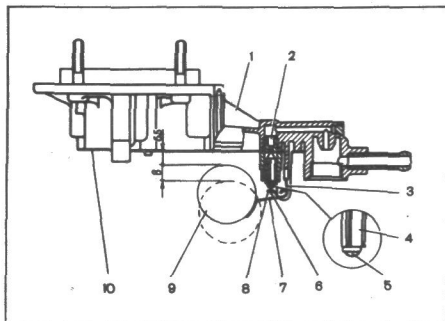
Установка уровня топлива в поплавковой камере карбюратора: 1 — крышка карбюратора; 2 — седло иглы клапана; 3 — упор; 4 — иглы клапана; 5 — шарик; 6 — оттяжная вилка; 7 — рычаг; 8 — язычок; 9 — поплавок; 10 — прокладка
